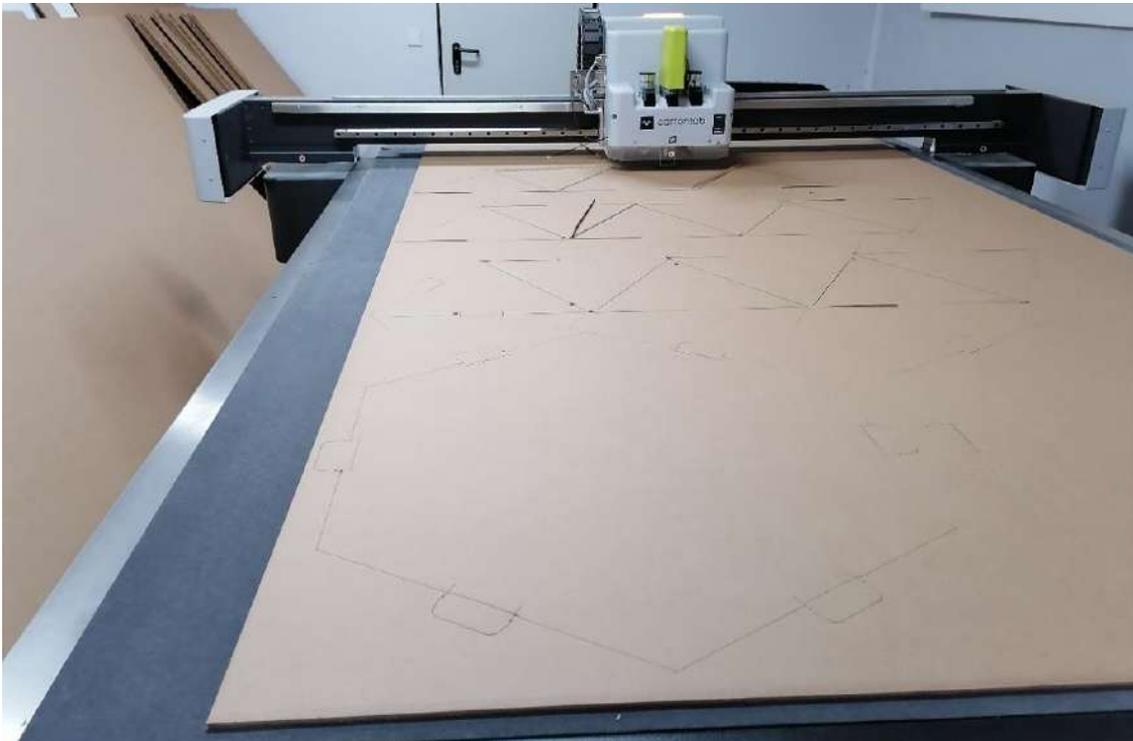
Fotografía del área de corte donde podemos ver la máquina de corte configurando las piezas de un modelo. Autor: Bruno Aguilar.
